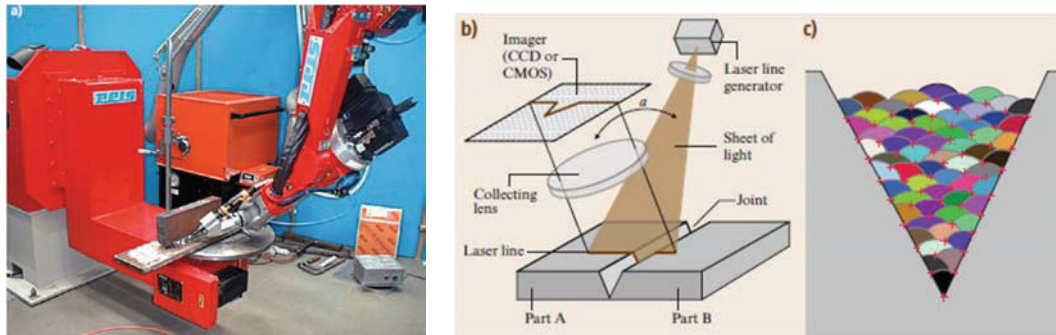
Robot de Soldadura con su sensor de guía.
